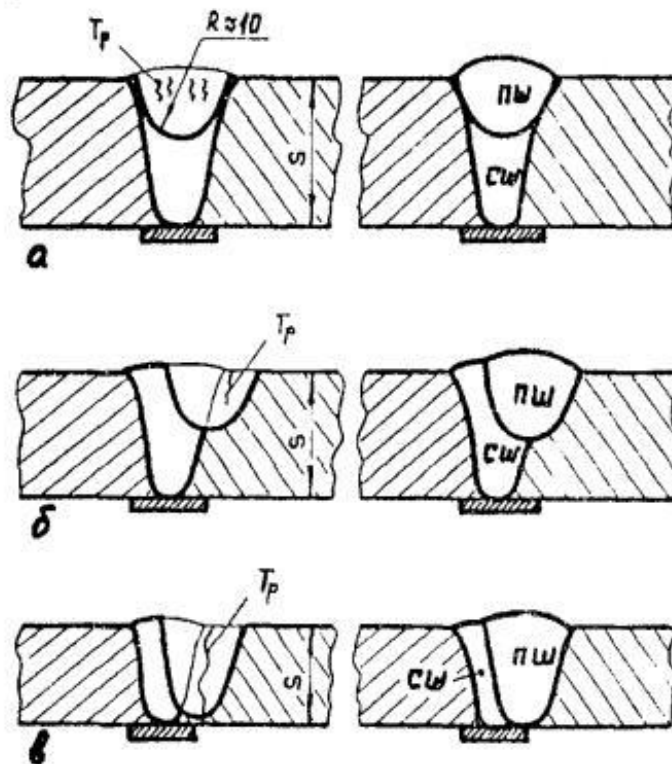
Схема выполнения ремонта сварного соединения с выборкой и последующей заваркой
